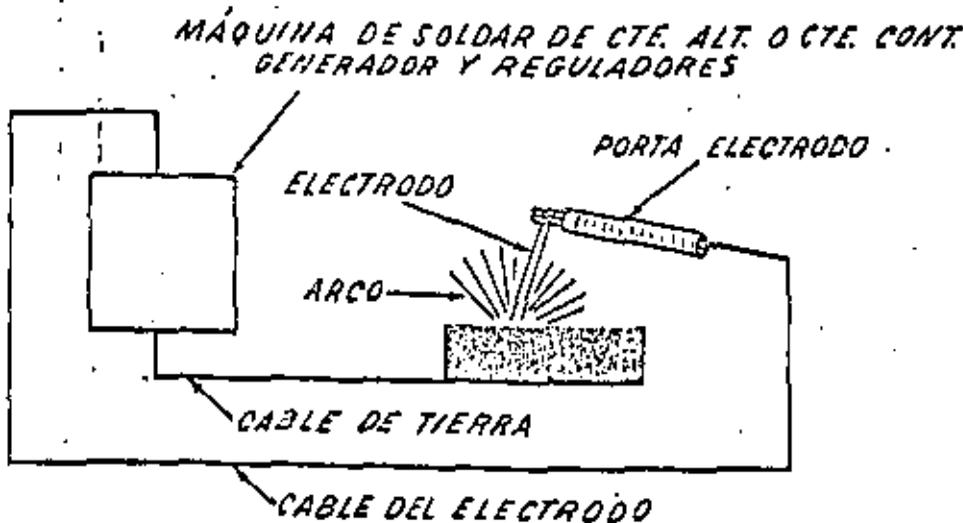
EL CIRCUITO DE SOLDADURA.
